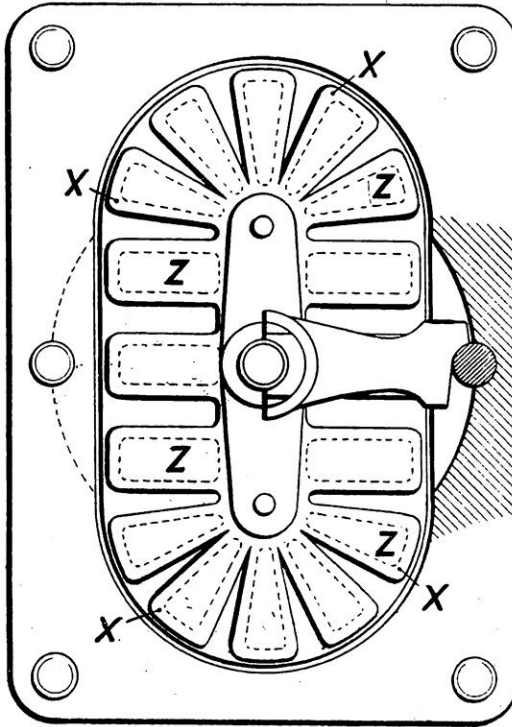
VUE EN PLAN DU CLAPET DE REFOULEMENT
